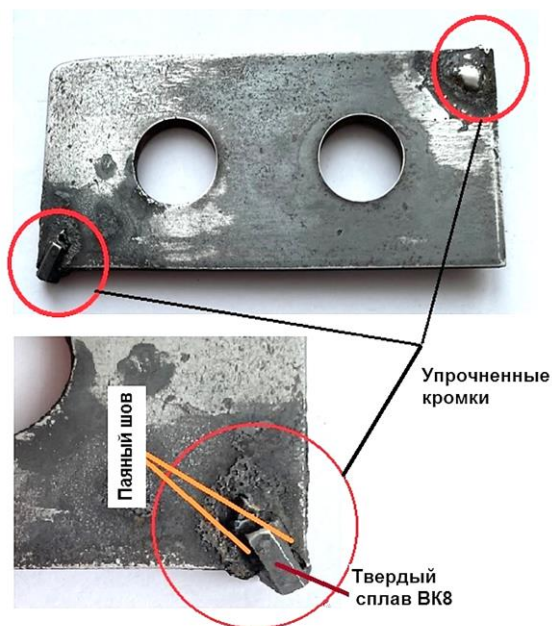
Образец молотка с упрочненной рабочей кромкой
